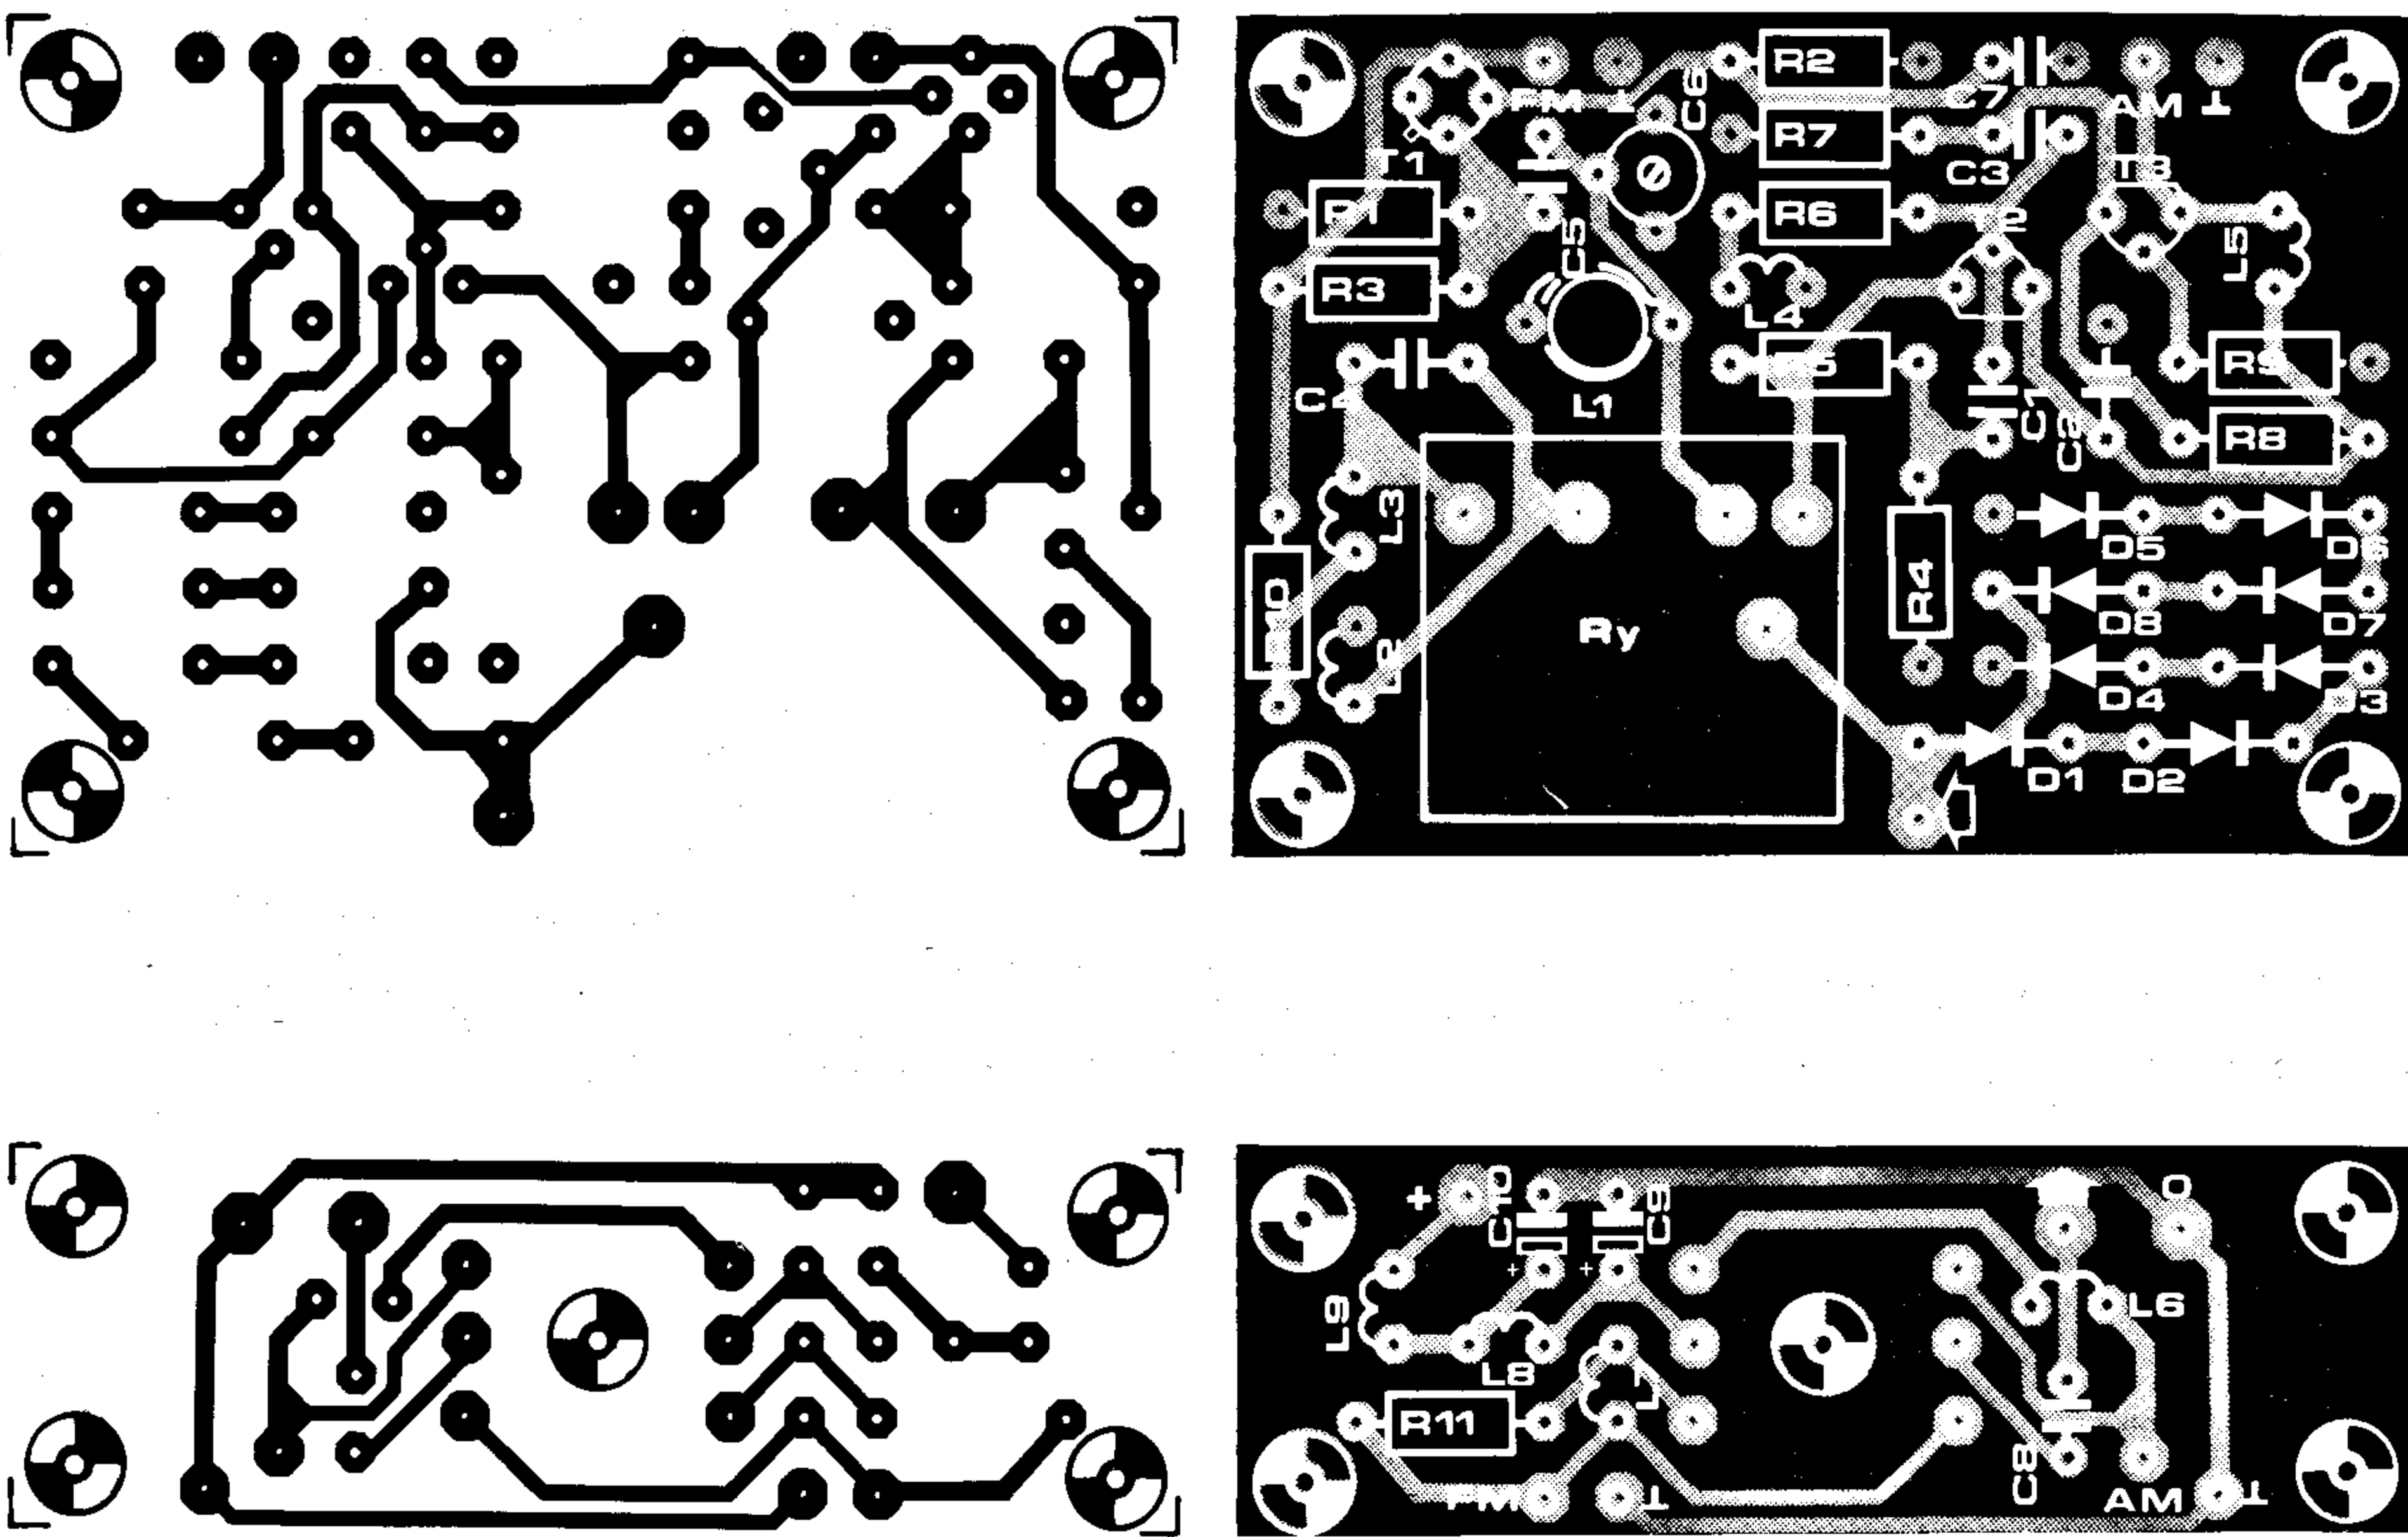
Placas de circuito impreso y disposición de componentes; (a) para la sección amplificadora, (b) para la sección de filtros e inversor. La placa (b) deberá montarse cerca del aparato de radio, de forma que el interruptor sea accesible. La placa (a) se montará lo más cerca posible de la antena.
